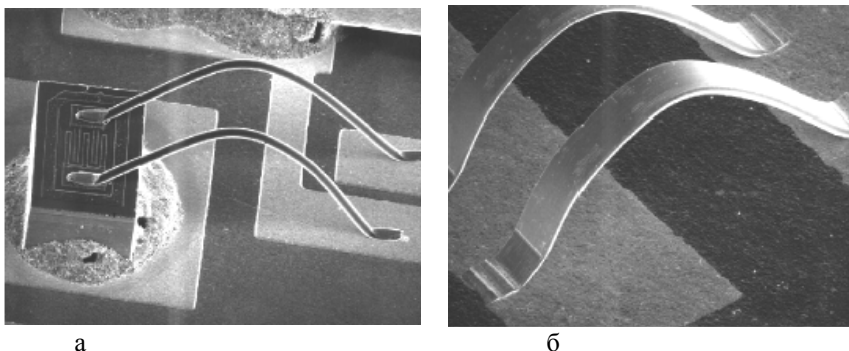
Сварные соединения проводниками круглого и плоского сечения
